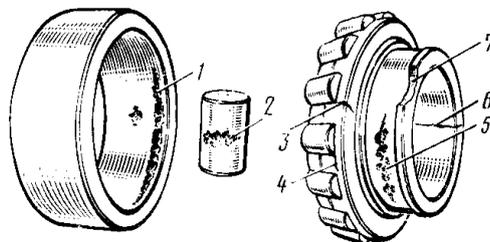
Дефекты деталей роликового подшипника: 1 – раковины на дорожке качения наружного кольца; 2 – раковины на цилиндрическом ролике; 3 – излом сепаратора; 4 – трещина у основания перемычки; 5 – раковины на внутреннем кольце; 6 – трещина кольца; 7 – откол борта кольца.
